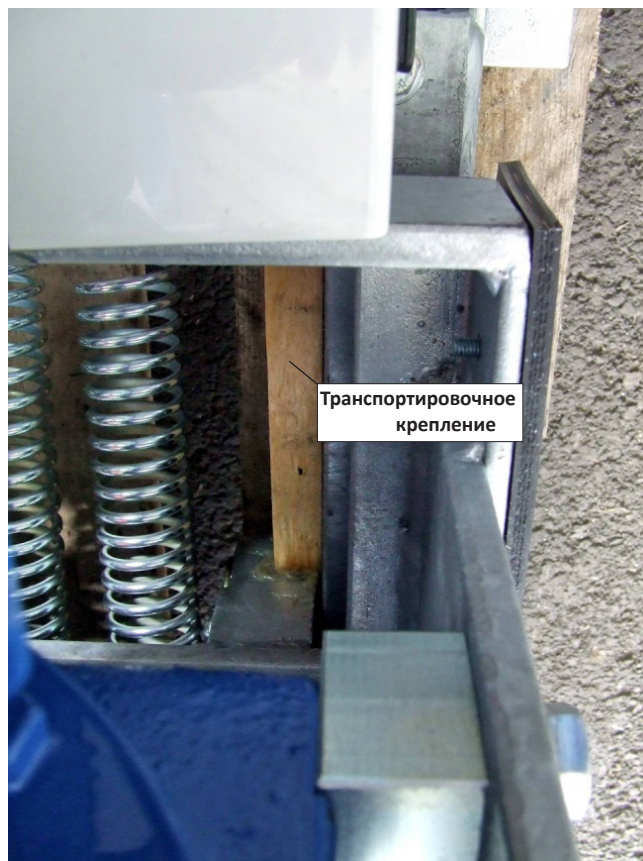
Положение транспортировочного крепления (вид сверху)
